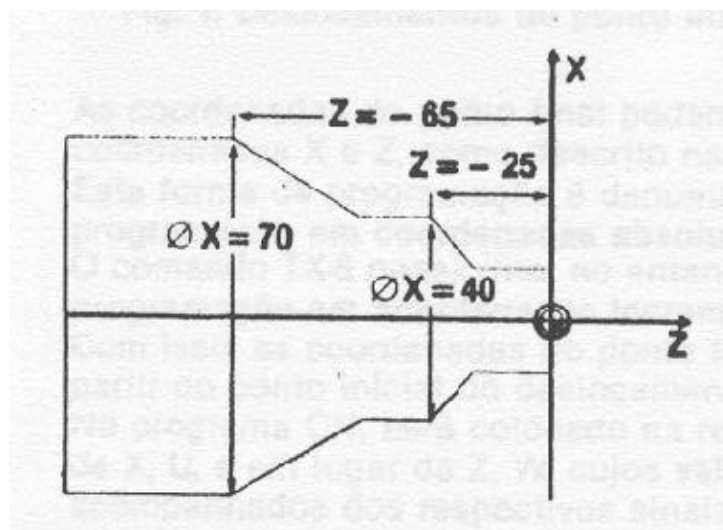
Sistema de Coordenadas (adaptado de IFAO,1984)
